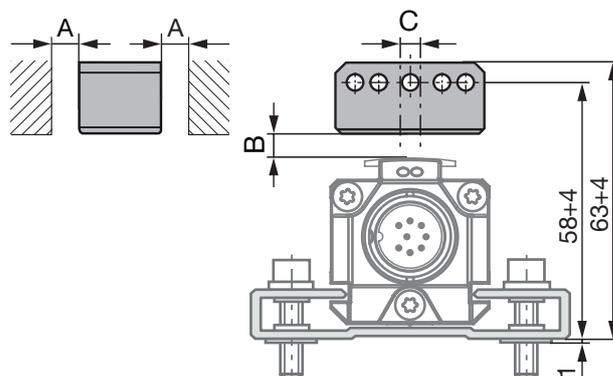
Dimensions et distances pour le capteur de position BTL6-A-3801-2
